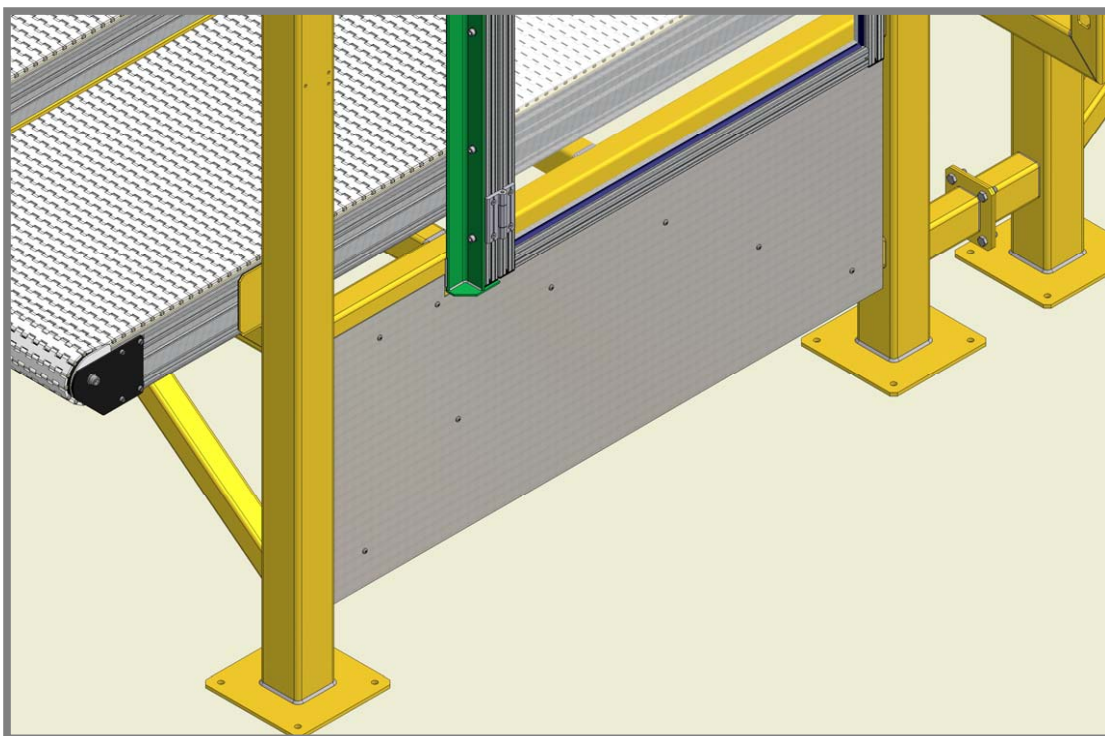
Mechanismus „ball catch“.Obr. 7-36 Umístění mechanismu „ball catch“.
